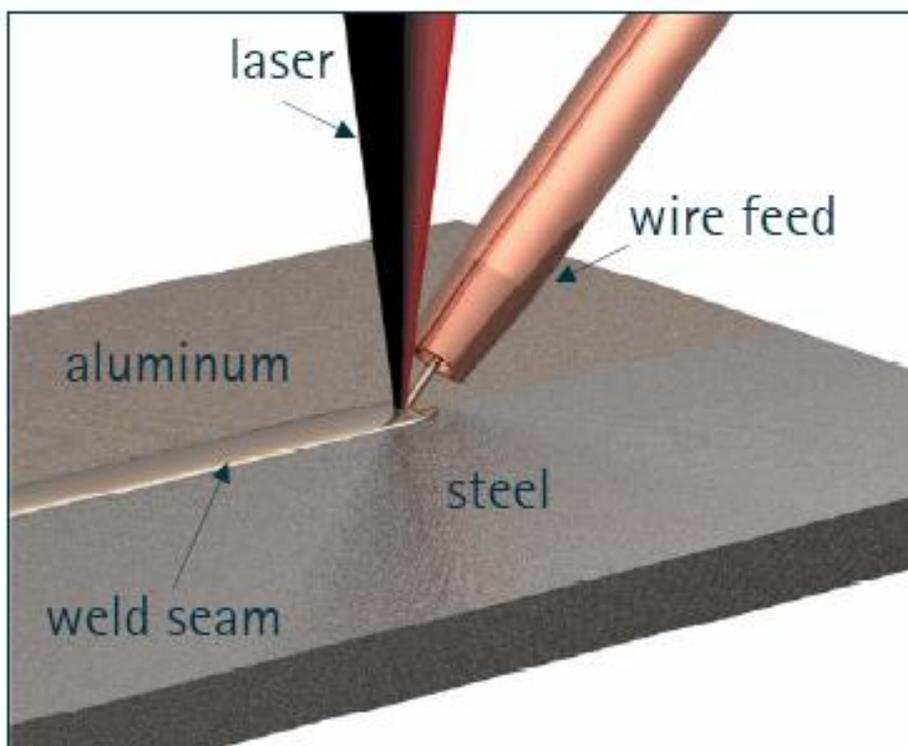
Laserschweißen von Stahl und Aluminium
